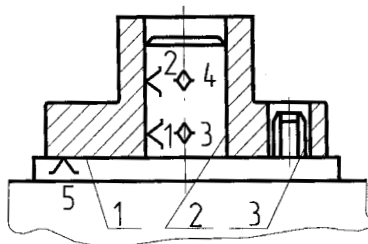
Базирование корпусной заготовки на плоскость, длинное отверстие и отверстие малого диаметра во фланце
